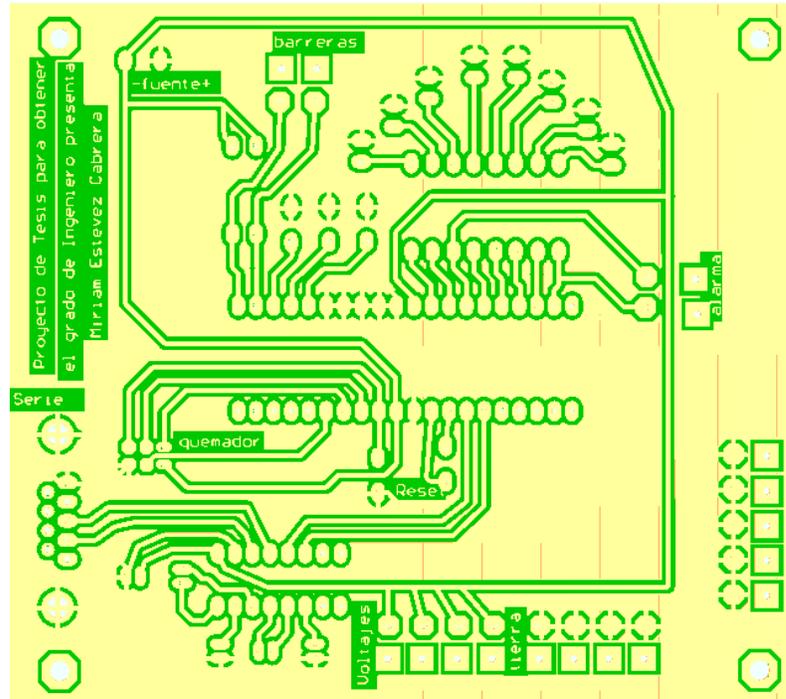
Placa PCB cara inferior (*bottom layer*)
